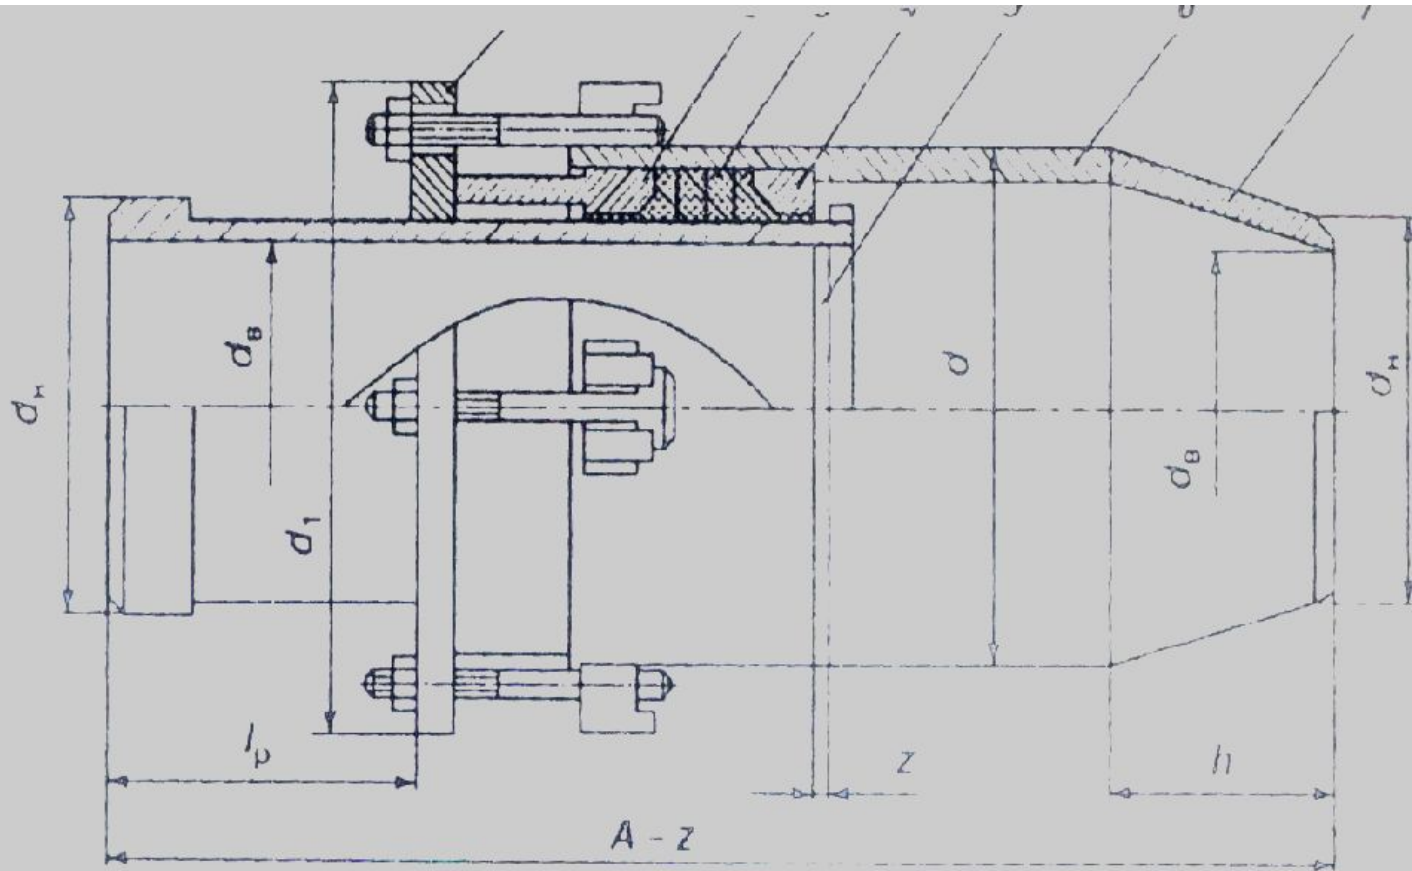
Односторонний сварной сальниковый компенсатор
